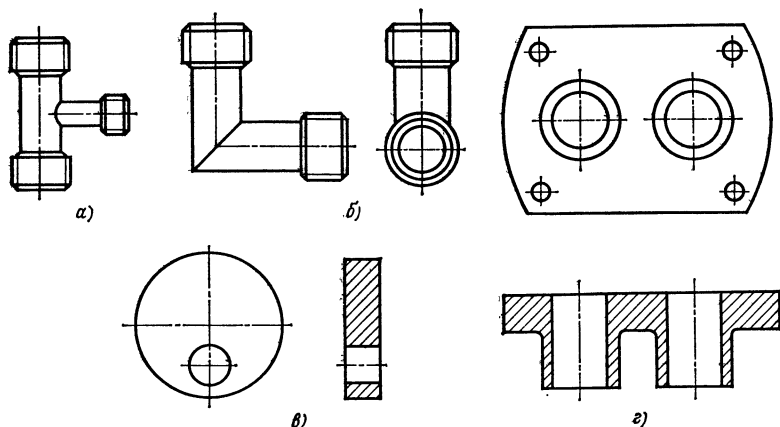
Виды деталей, обрабатываемые в анализируемых приспособлениях:
